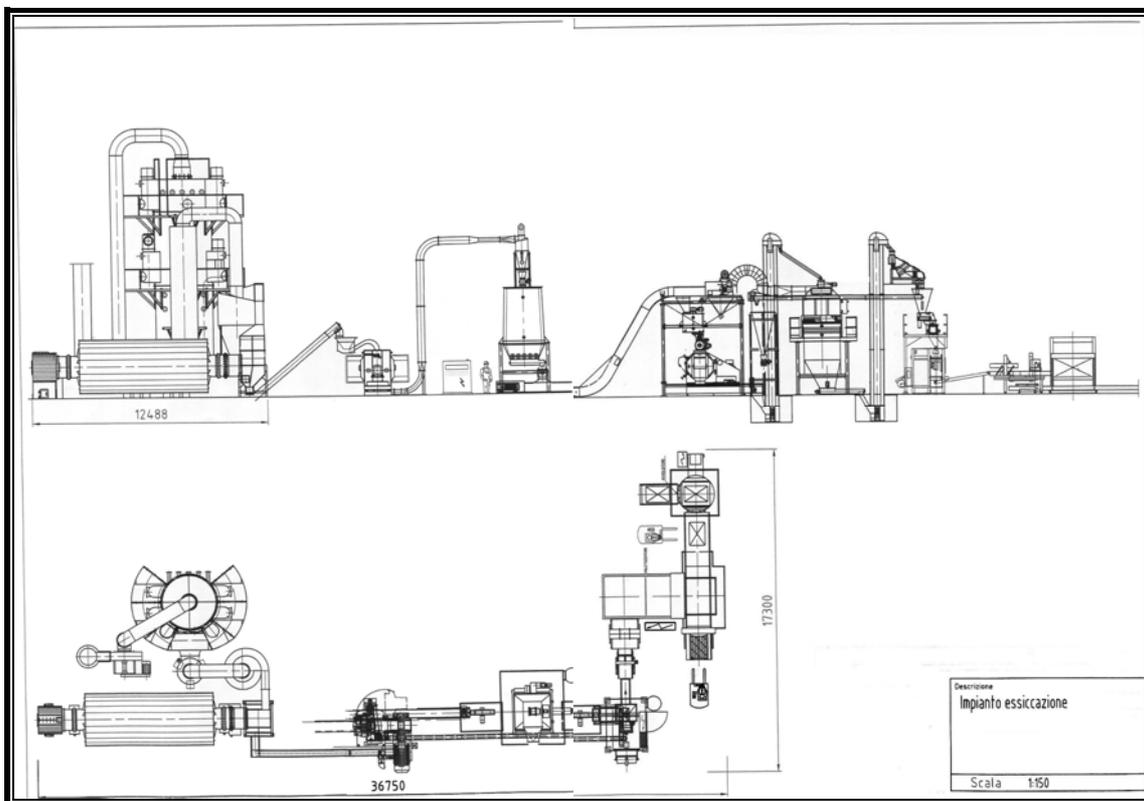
Disegno e dimensioni dell'impianto essiccatore
